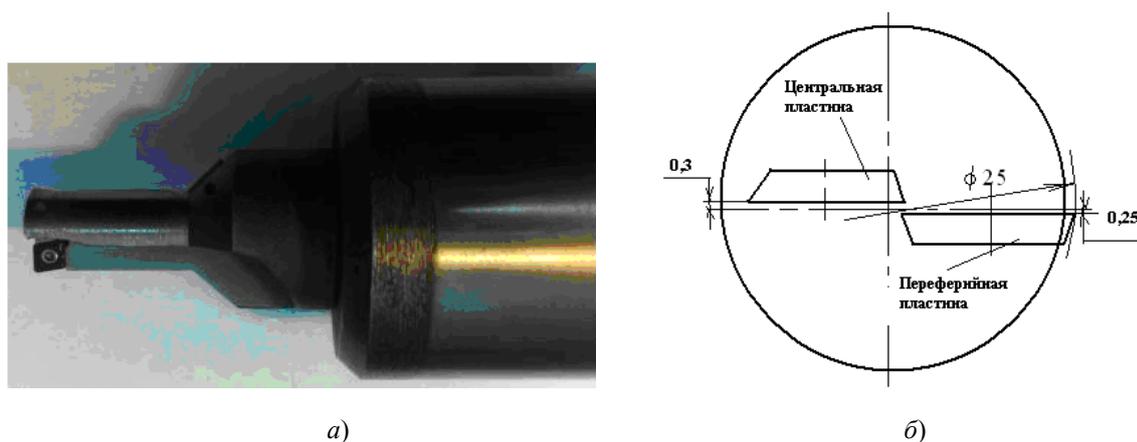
Конструкция сверла: а – общий вид сверла в оправке; б – расположения СМП в корпусе
